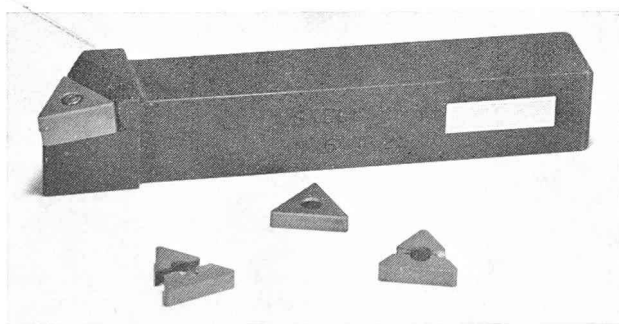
Vue du porte-outil et des plaquettes défectueuses.
